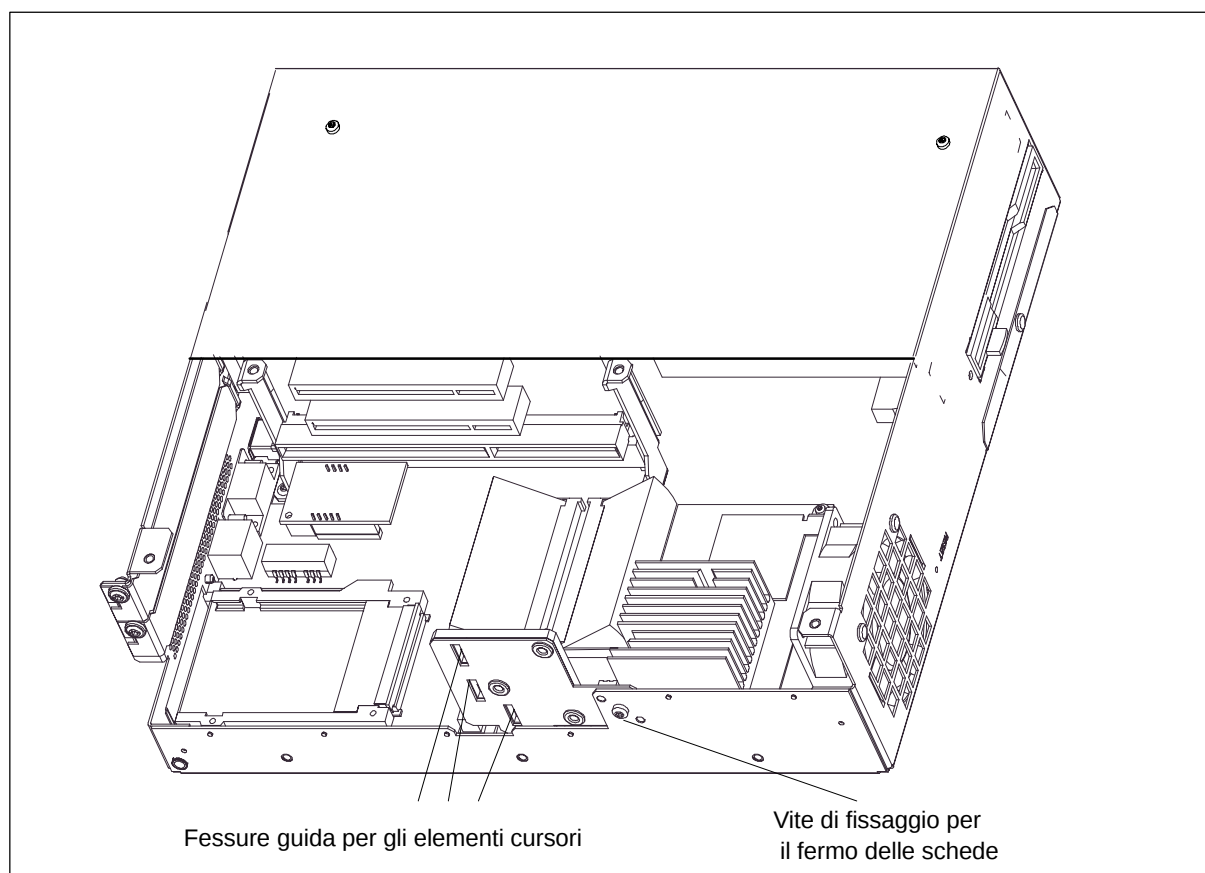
Smontaggio e montaggio di una scheda di ampliamento
